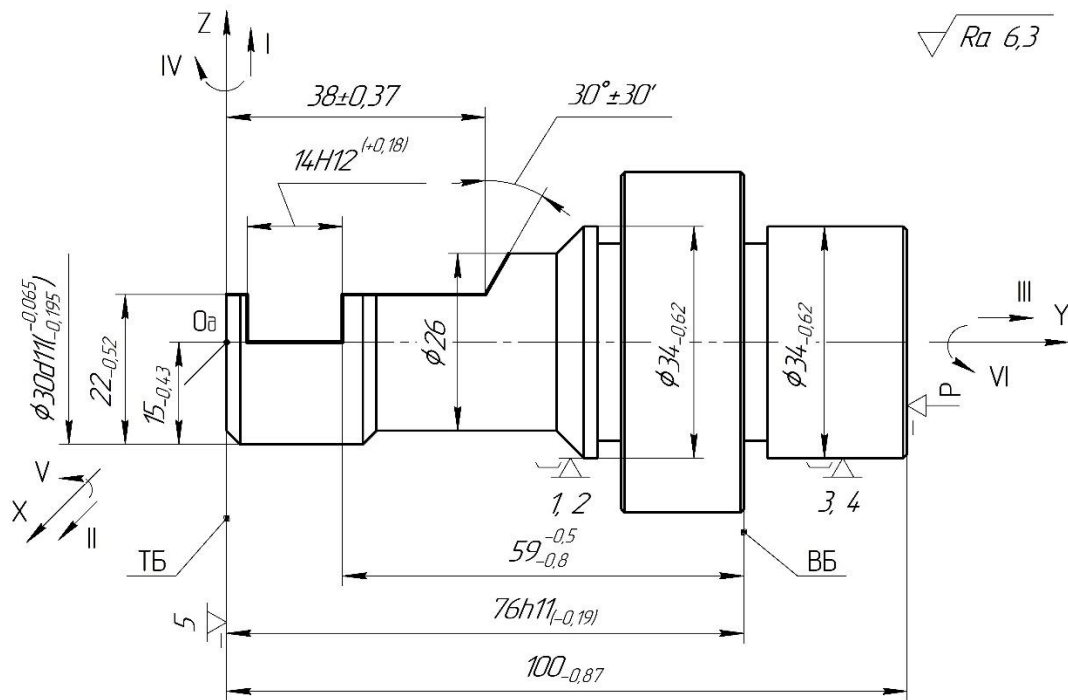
Базування заготовки на операції 020 «Фрезерна з ЧПК». Схема №2
